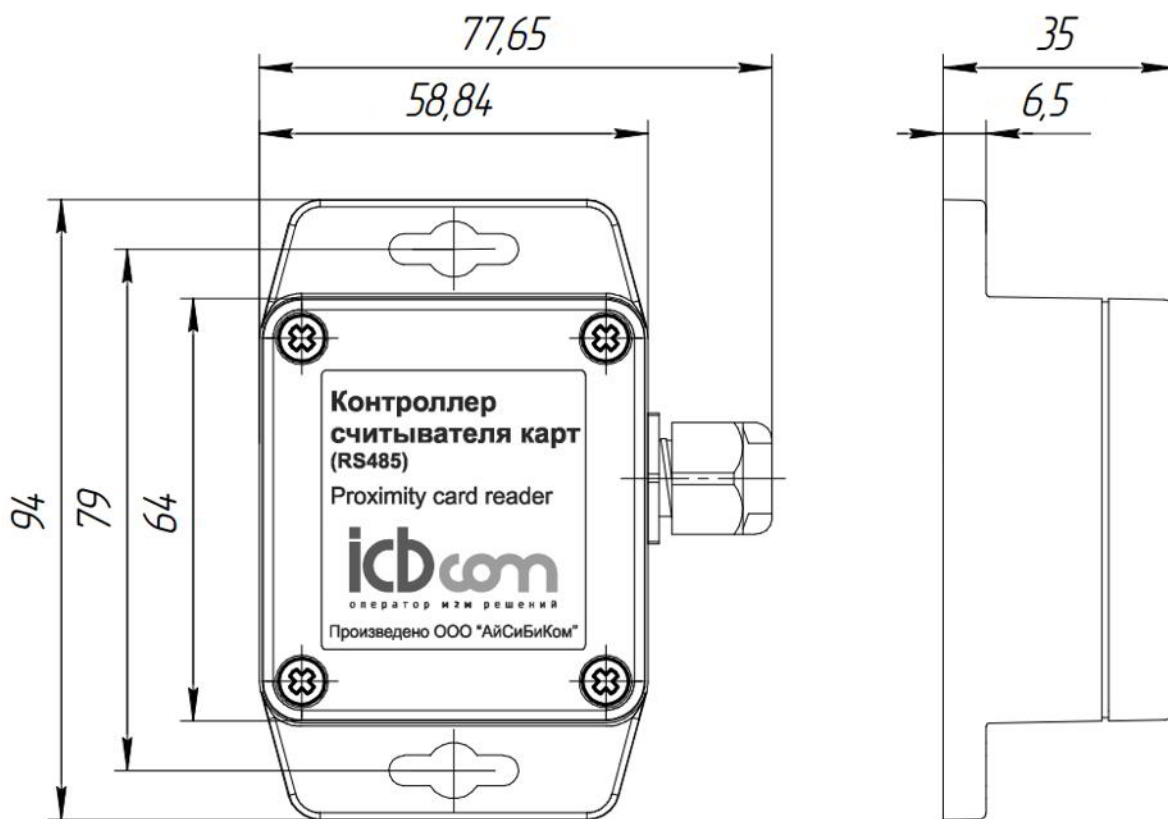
Габаритные размеры контроллера считывателя карт
